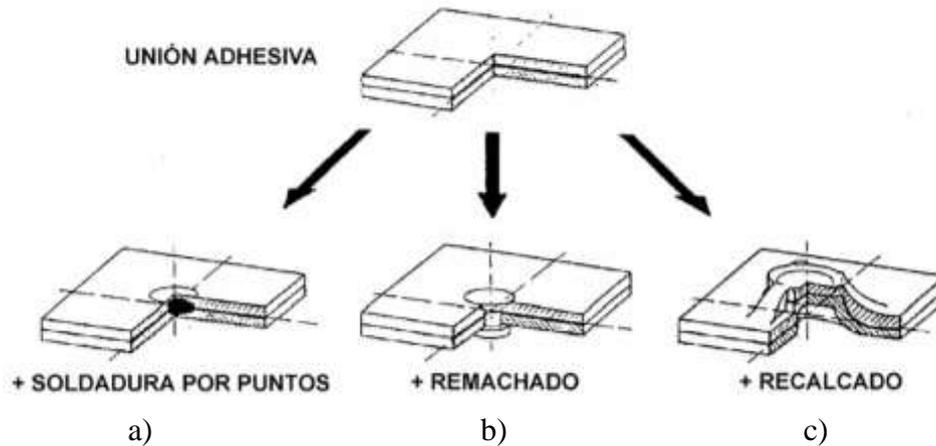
Tipos de uniones mixtas: a) Adhesivo más soldadura. b) Adhesivo más remachado. c) Adhesivo más recalado.
